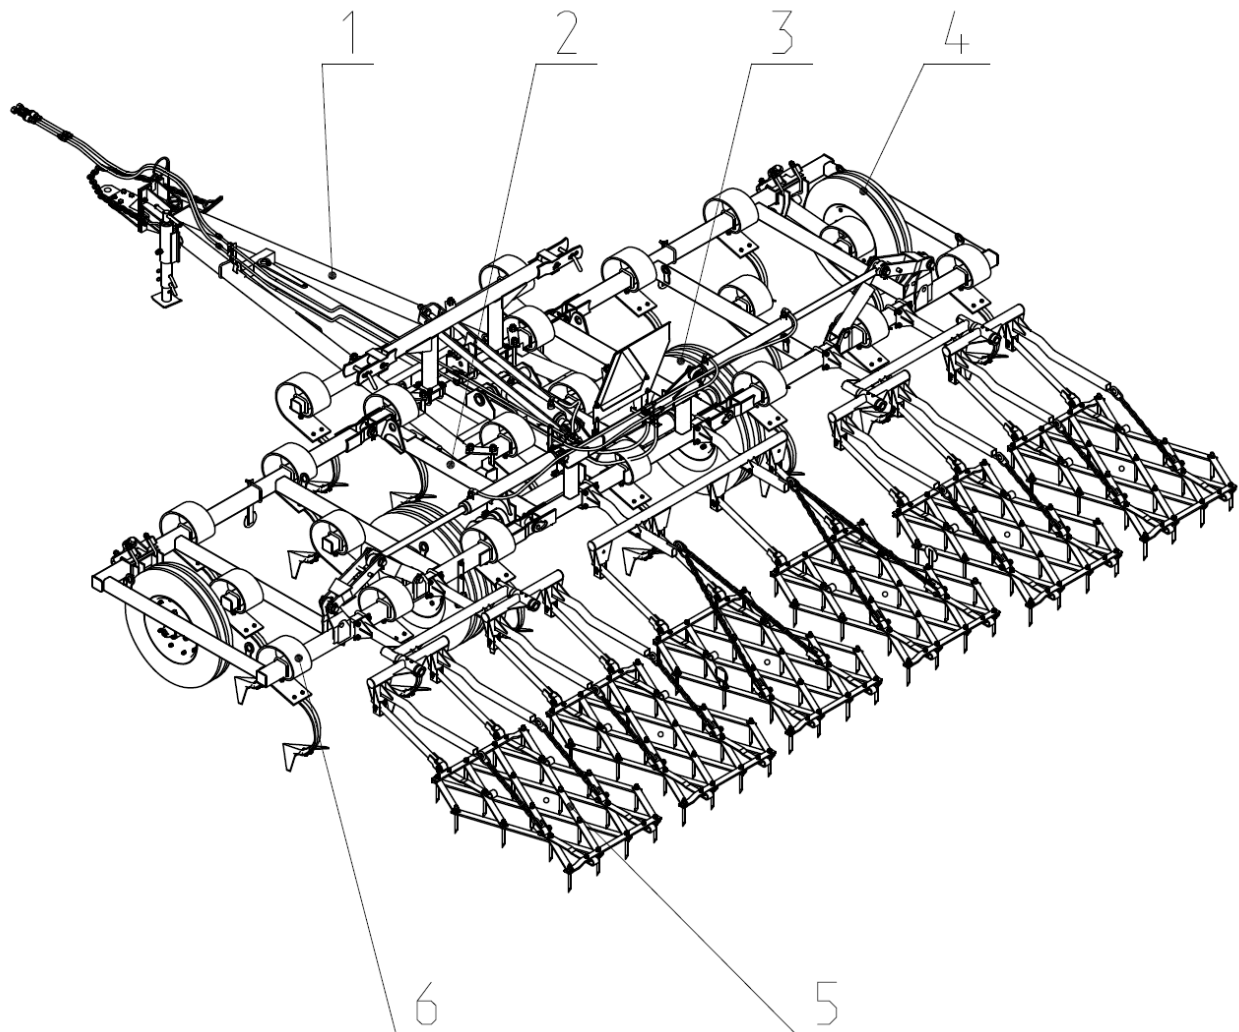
КСП-6 Культиватор с комплектом КСП 05.000В приспособлением для навески зубовых борон.
